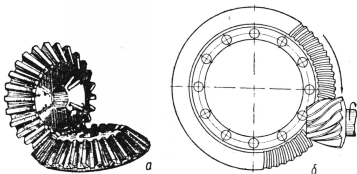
Конические зубчатые колеса: а — с прямым зубом; б — со спиральным зубом (гипоидное).
